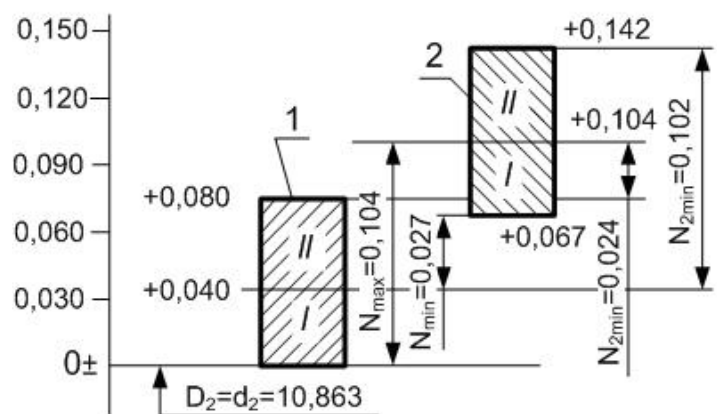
Схема розташування полів допусків нарізного з'єднання M12-2H5C(2)/3p(2): 1-поле допуску D_2 , 2-поле допуску d_2
